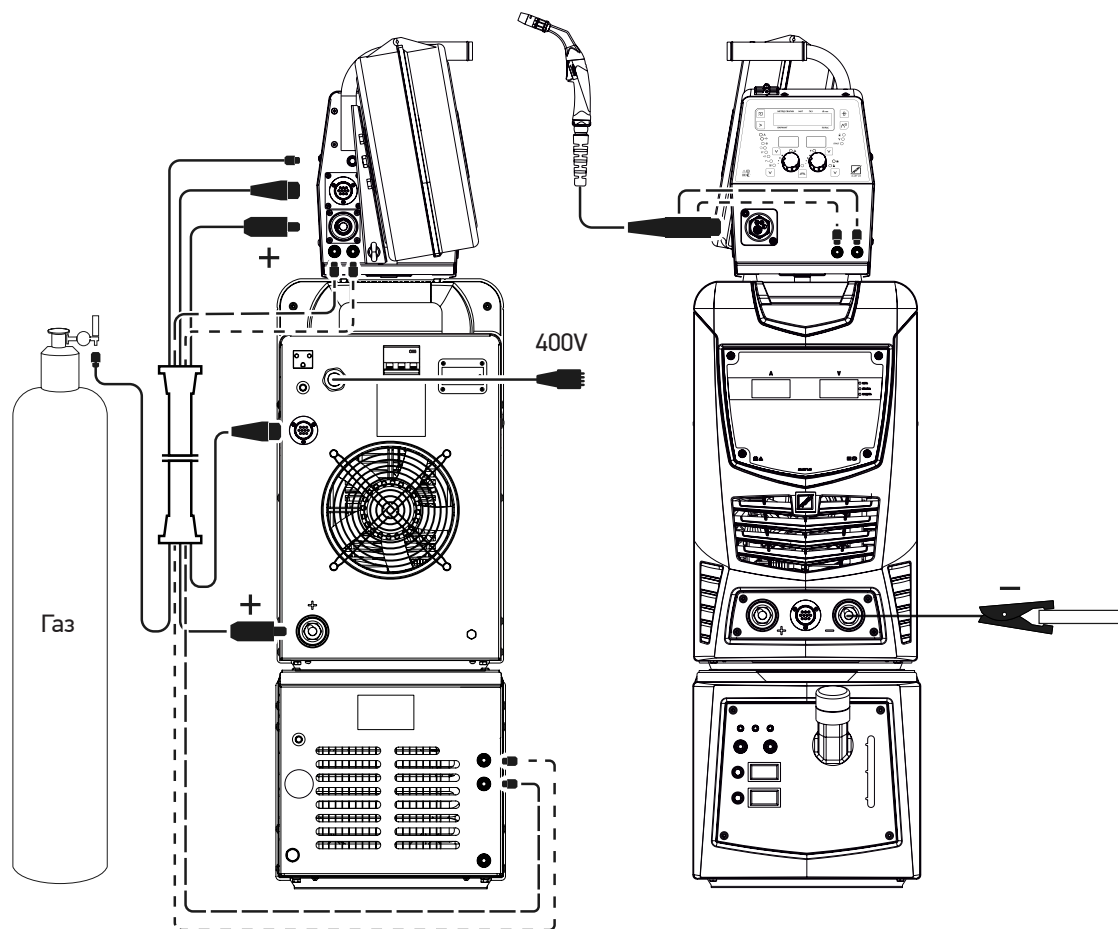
Возможная схема соединений комплекта сварочного оборудования MIG/MAG.
